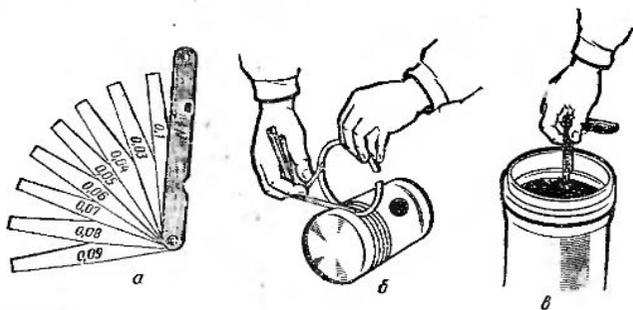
Набор щупов (а) и проверка щупами зазоров между канавкой поршня и поршневым кольцом (б) и в стыке поршневого кольца, помещенного в гильзу цилиндра (в).
